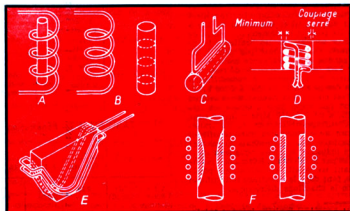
Disposition des courants et des bobines pour obtenir un chauffage uniforme, d'après Jordan.
